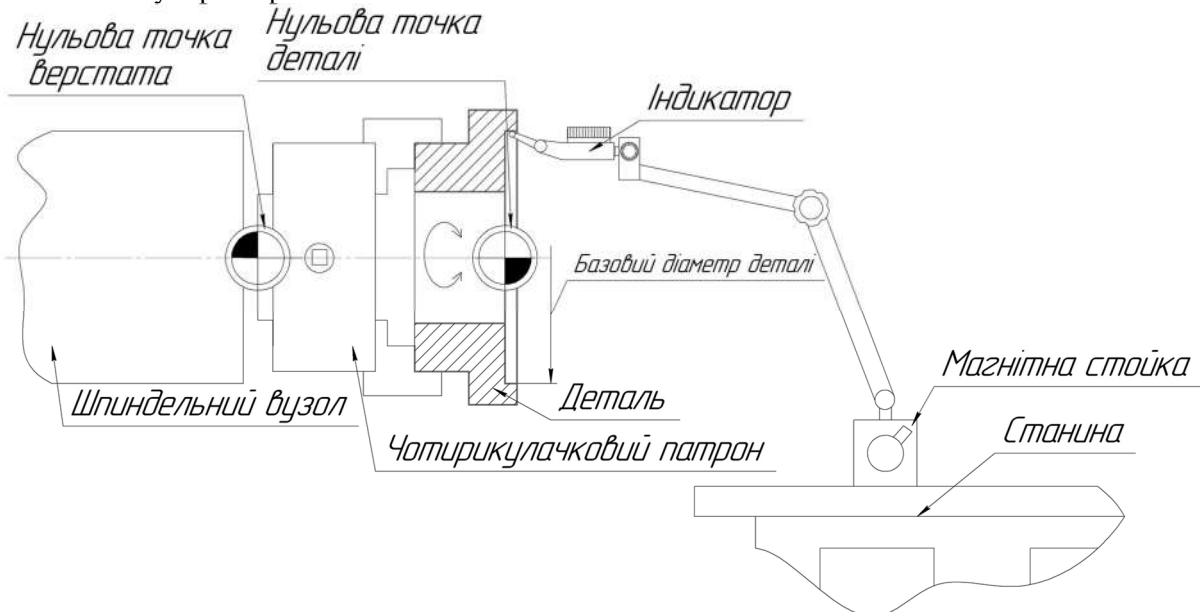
Приклад вивірки пристосування (деталі) на токарних верстатах
